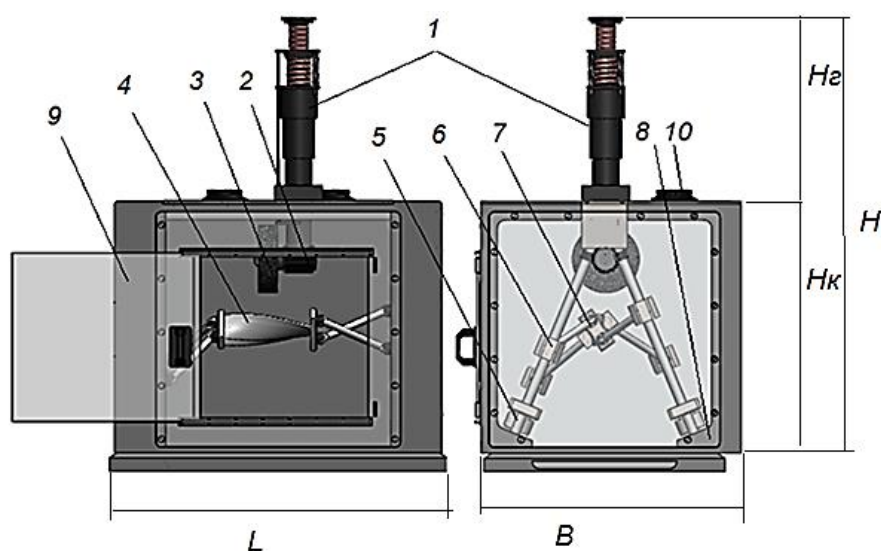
Предлагаемая компоновка станка для финишной обработки рабочей поверхности пера лопатки: 1 – силовая головка шлифовальная с электромагнитным приводом подачи; 2 – электродвигатель вращения абразивного круга; 3 – абразивный круг; 4 – заготовка (лопатка); 5 – шаговый двигатель, обеспечивающий перемещение каретки 6; 7 – станочное приспособление для крепления заготовки; 8 – корпус станка; 9 – прозрачная дверца; 10 – вытяжка.
